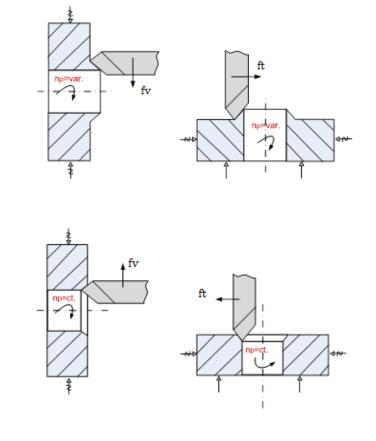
Plandrehverfahren / Procedee de strunjire plană [WES 10]
